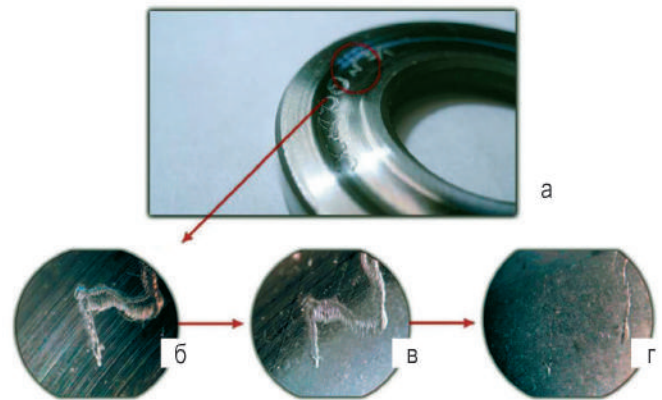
а) исходная поверхность подшипника с нанесенной маркировкой; б) дорожка качения подшипника с дефектом и следами шлифования; в) начало ревитализации поверхности; г) устранение поверхностного дефекта за счет модификации поверхности металлокерамическим покрытием
